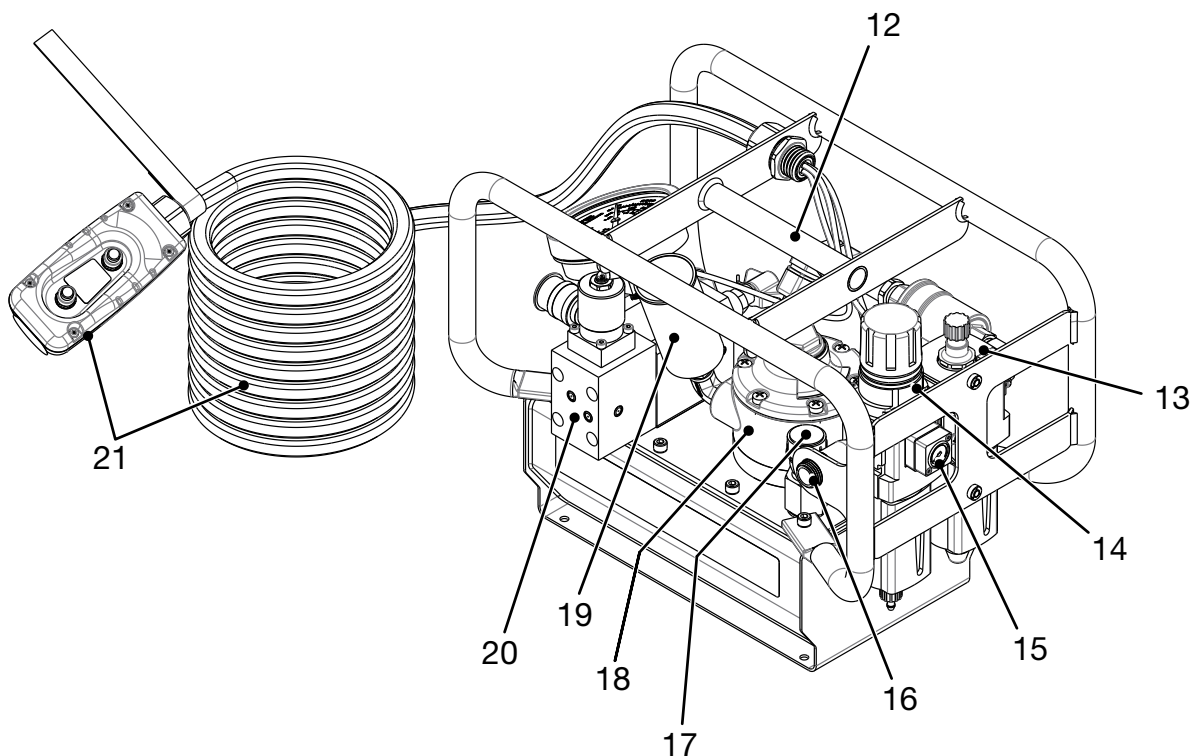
Wichtige Merkmale und Komponenten - Verschraubungspumpe der LAT-Serie
